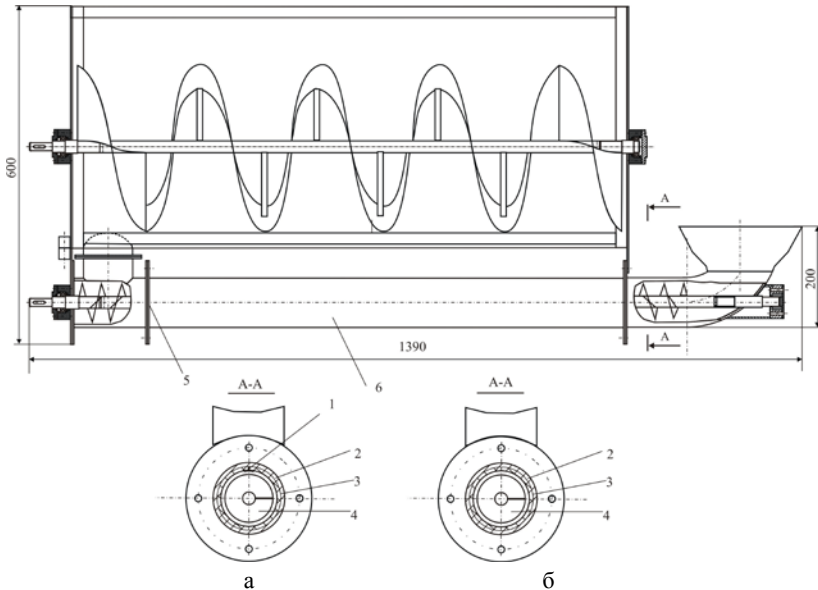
Чертеж конструкции питателя автомобильного газогенератора:
